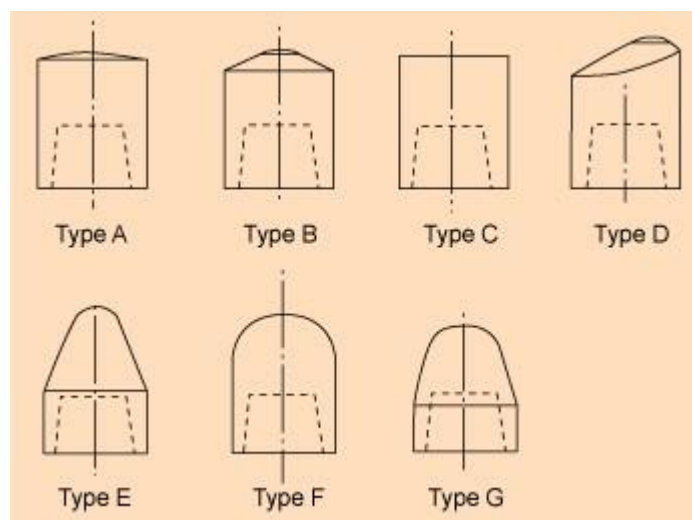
Formas alternativas de la punta del electrodo, normalmente utilizadas en las pistolas de soldadura por puntos portátiles. Fuente: TWI
